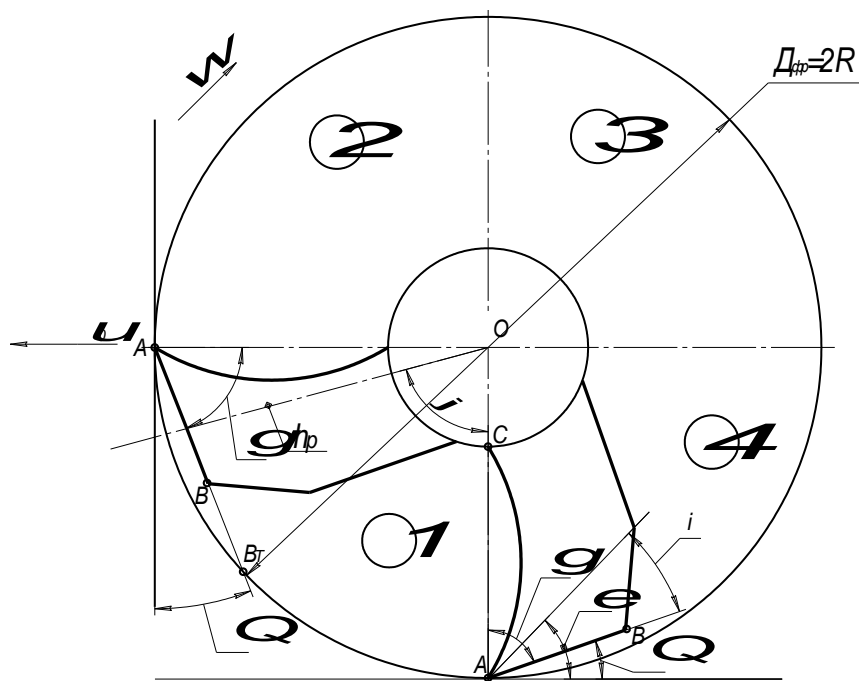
Геометрические параметры ножа фрезерного барабана
